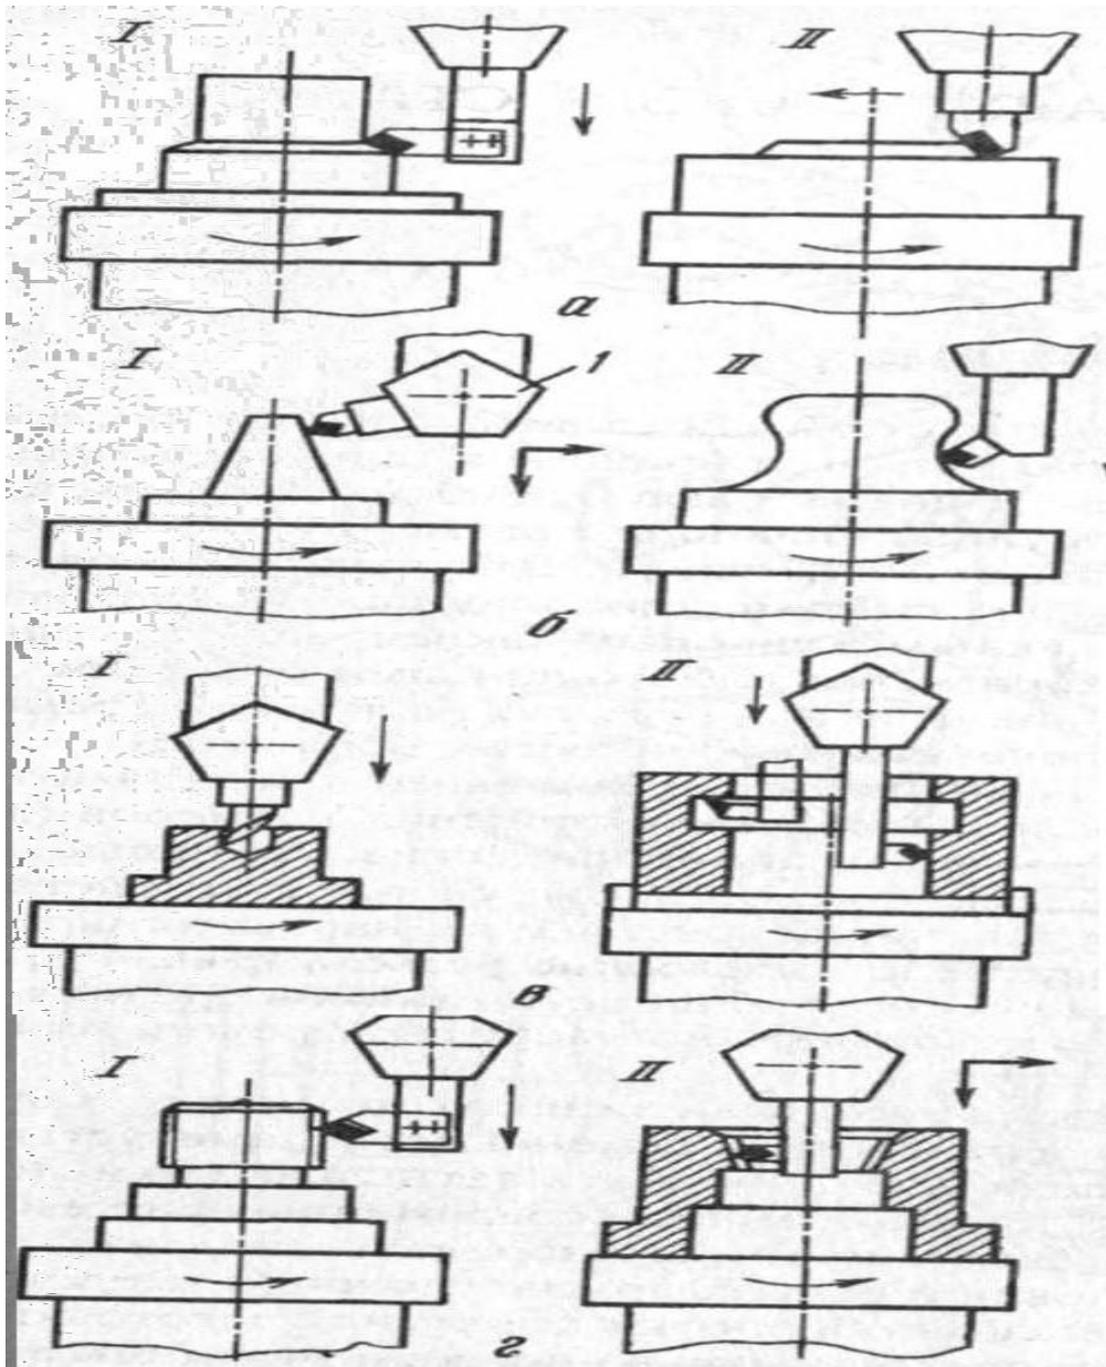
Схемы обработки различных поверхностей на токарно-карусельных станках.
